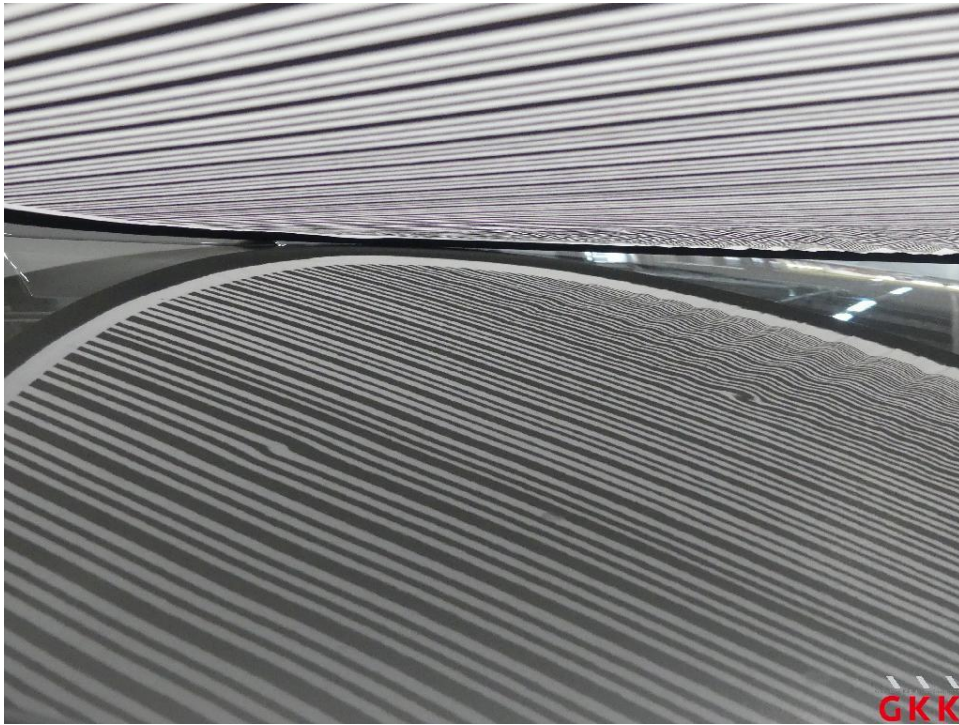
Dach, 4 bis 10 Dellen / Bauteil, kalt drücken
